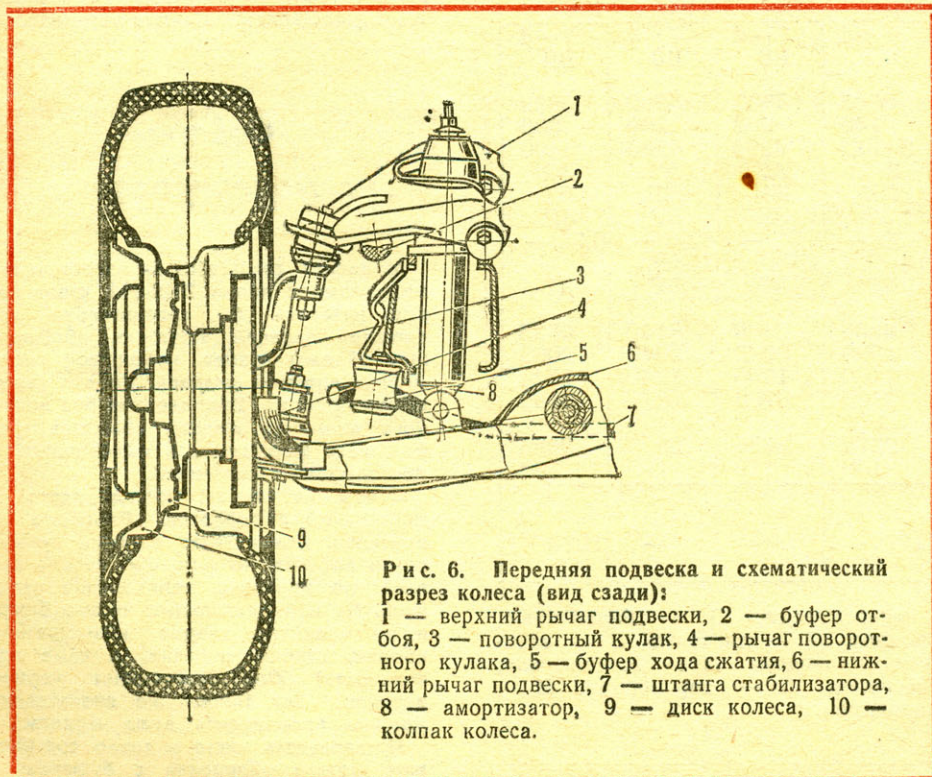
Передняя подвеска и схематический разрез колеса (вид сзади):
